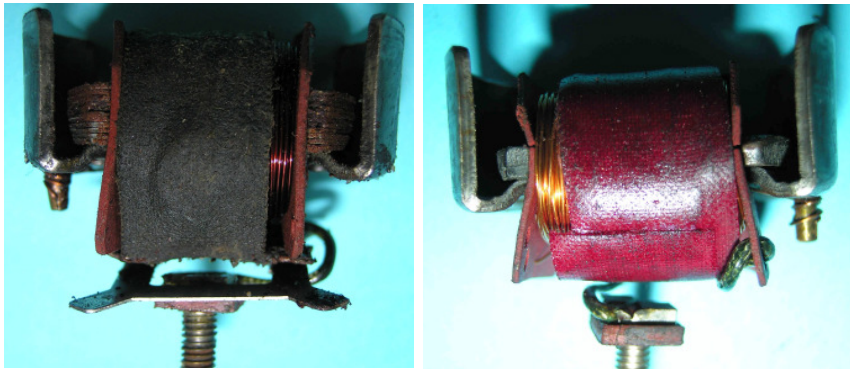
Ersatz des 6 mm starken Blechpakets durch ein 3 mm dickes Blech
